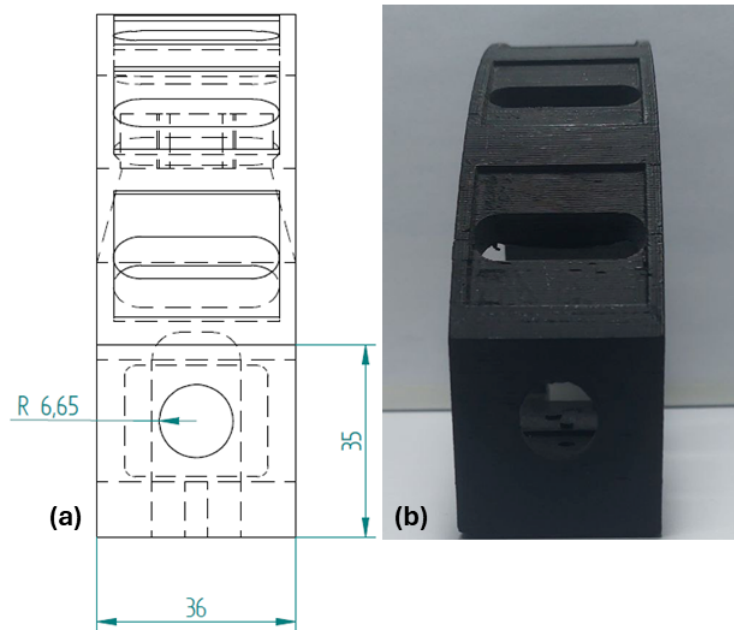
Vista frontal *ribs*: (a) Desenho técnico (b) Peça impressa.
